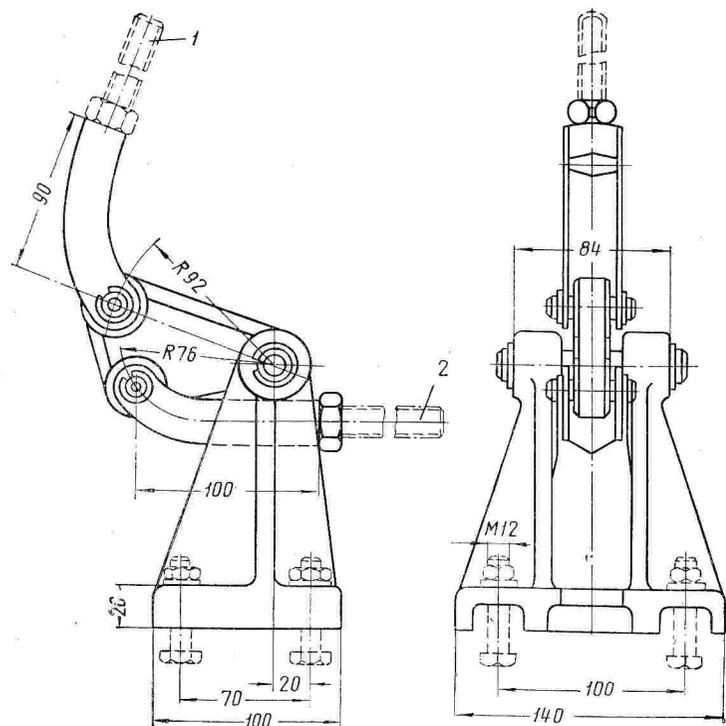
Подшипник типа ПДР для соединения выключателя типа ВМГ-133 с приводом ПРБА:
